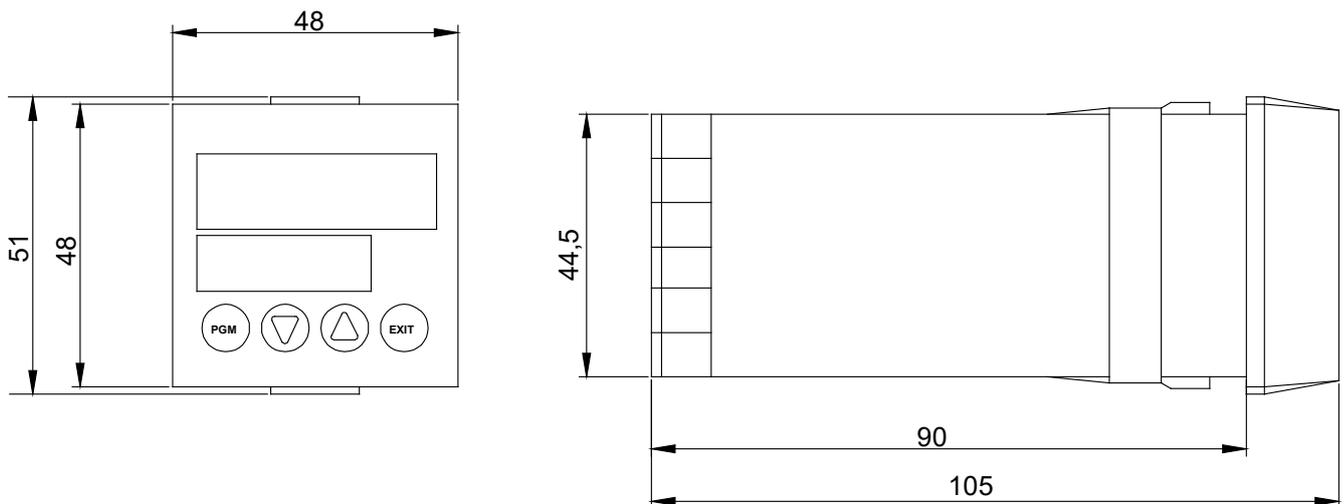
Gehäuseabmessungen und Montage Maße Regler 70304 für Frontplatteneinbau
